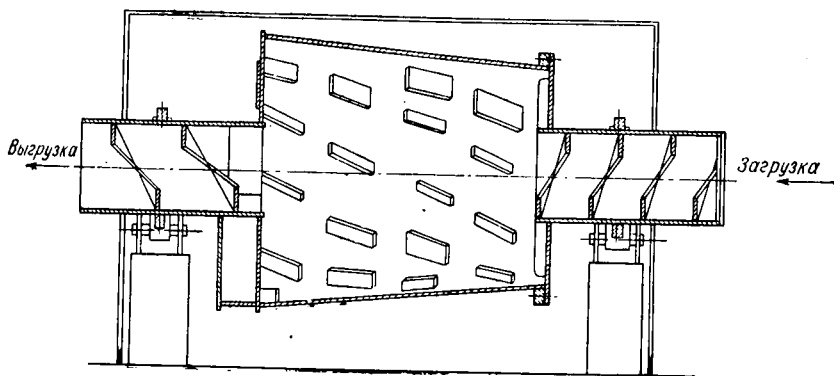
Барабанный реверсивный смеситель конструкции Гипрометиза
